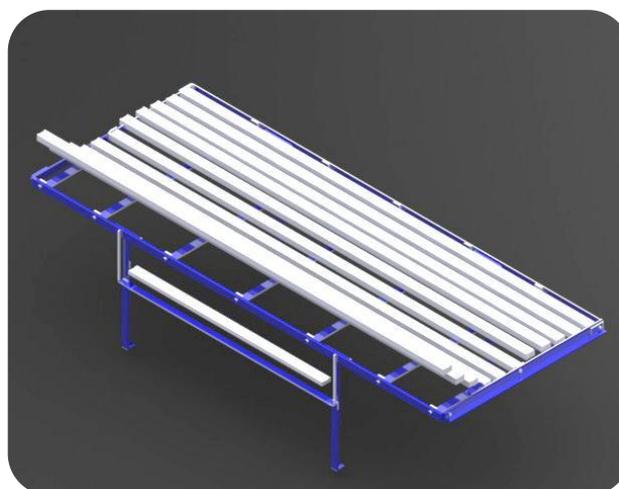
Escalón con patas plegadizas, peldaño y viguetas.
